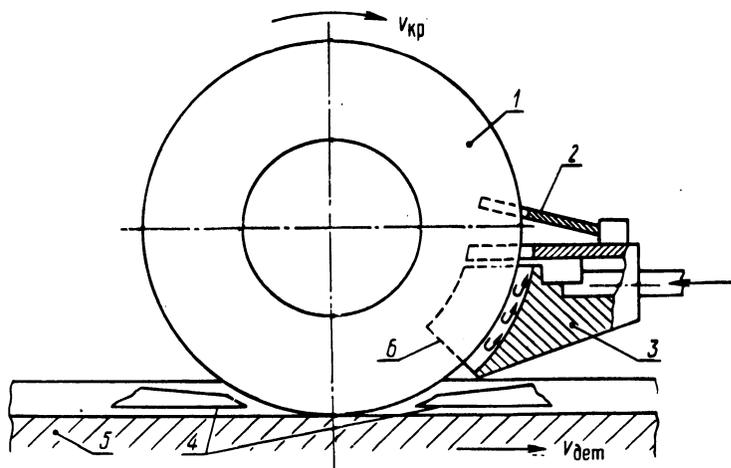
Схема устройства для подачи СОЖ при глубинном шлифовании пазов: 1 — шлифовальный круг; 2 — козырек для отражения воздушного потока; 3 — сопло для подачи СОЖ для очистки круга; 4 — сопла для подачи СОЖ в зону резания; 5 — обрабатываемое изделие; 6 — щиток.
